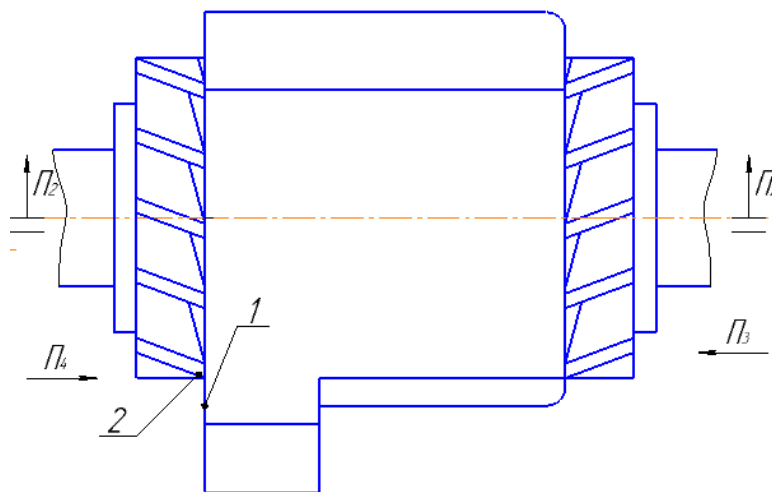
Схема формоутворення при фрезеруванні торців деталі
